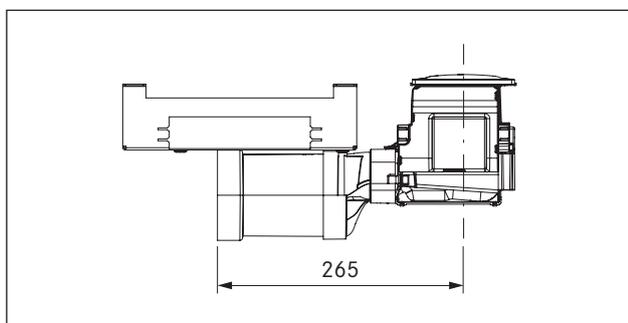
Niveau de raccordement de canaux PKA avec section droite
